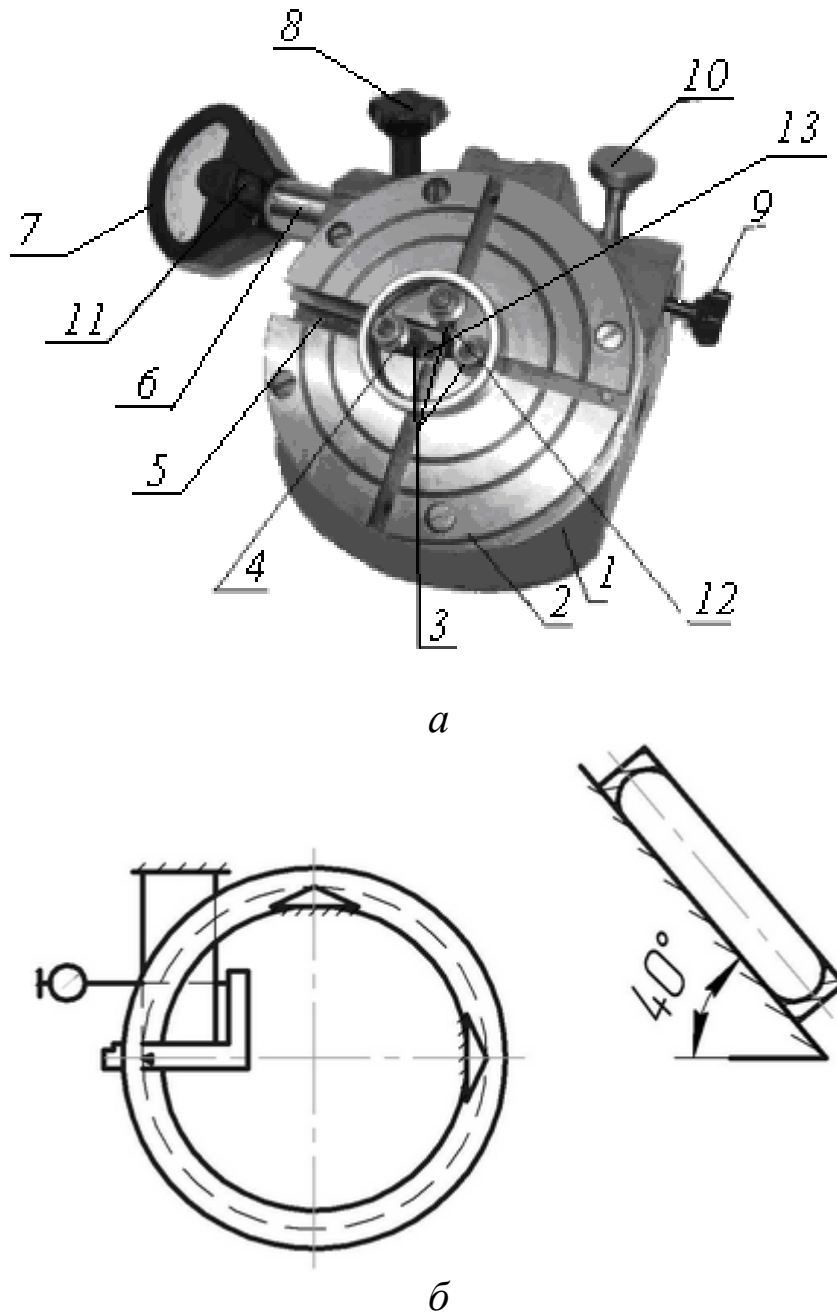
Фото прибора УД-1В (*а*) и схема измерений (*б*) диаметра желоба наружного кольца подшипника
